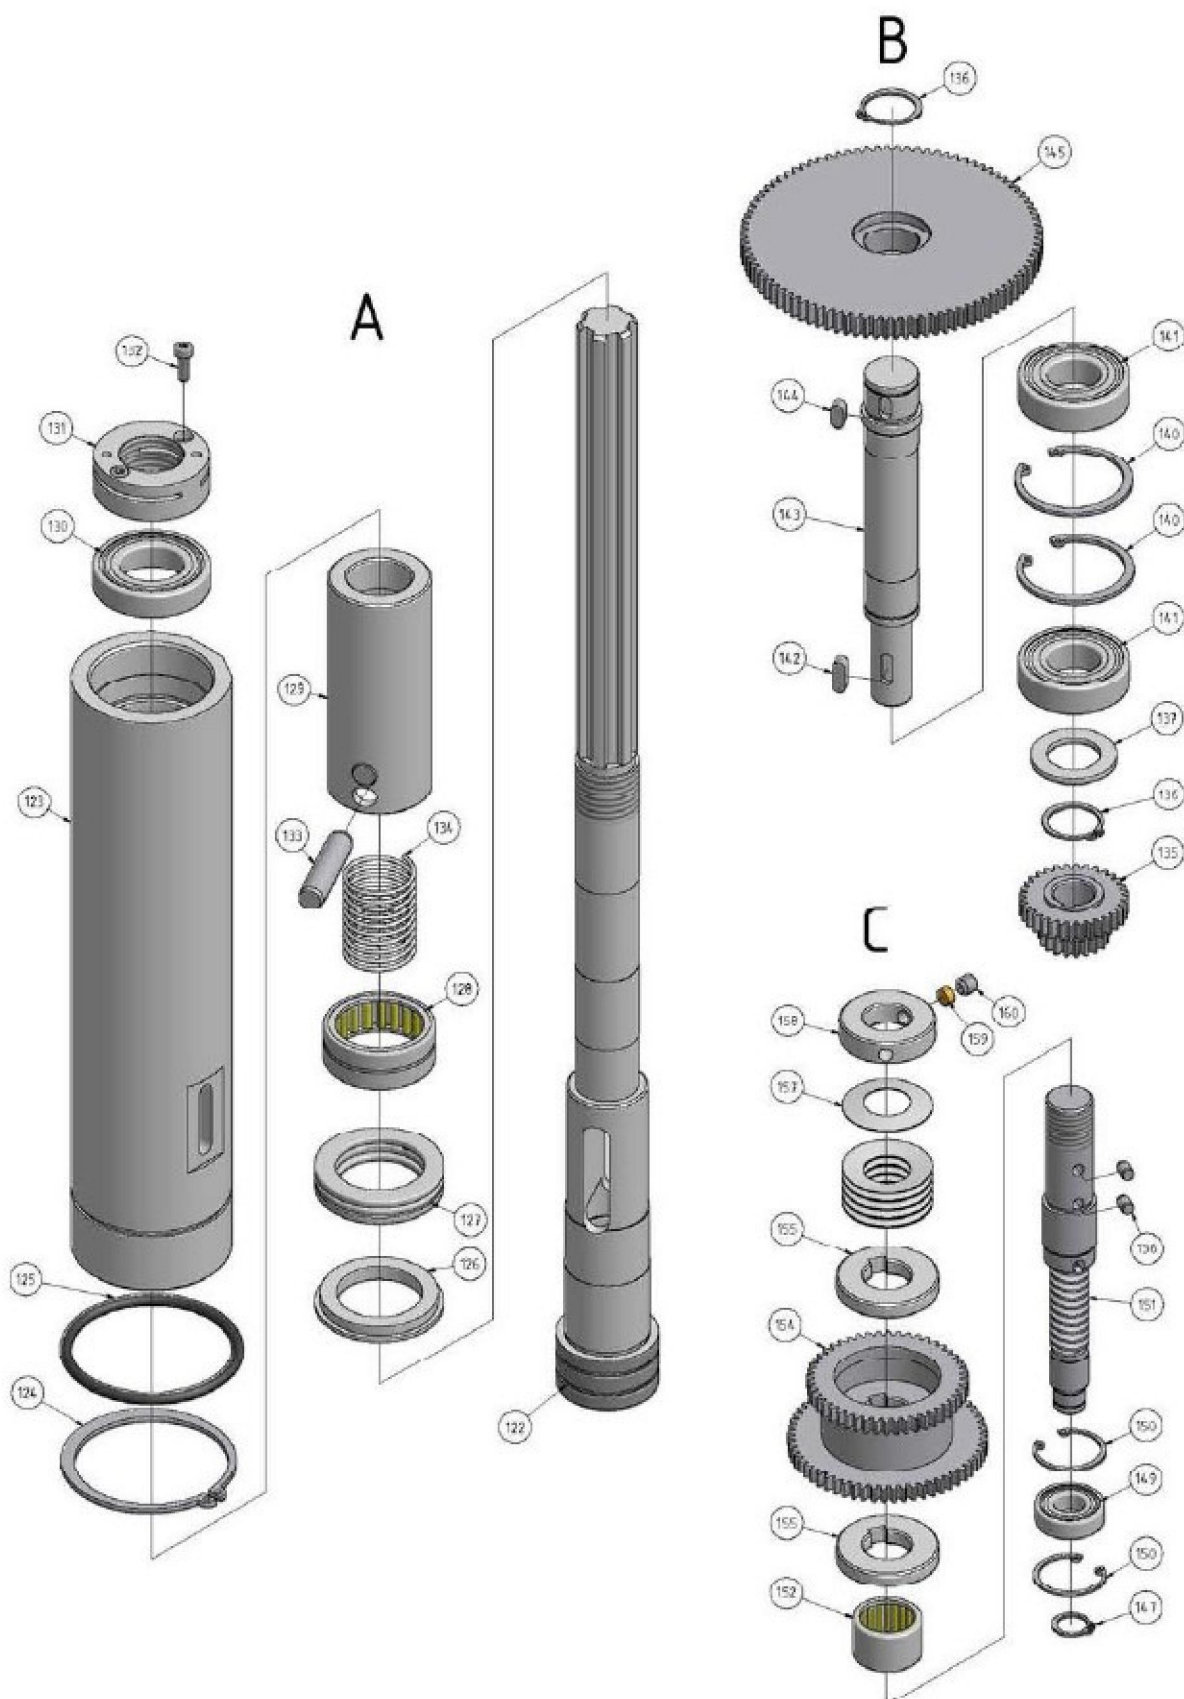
Caja de engranajes de avance 1 de 4 - Feed gear box 1 of 4
